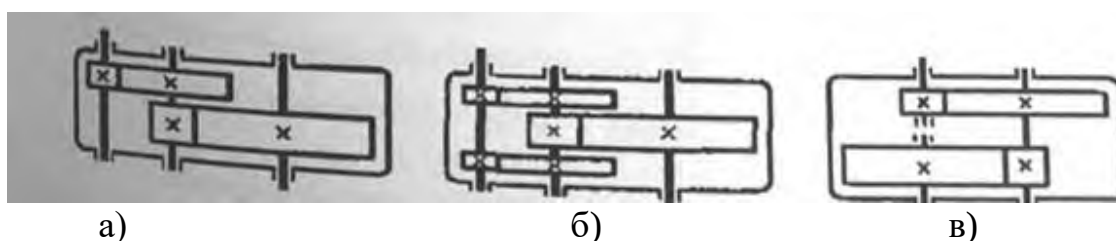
Кинематические схемы цилиндрических двухступенчатых редукторов
